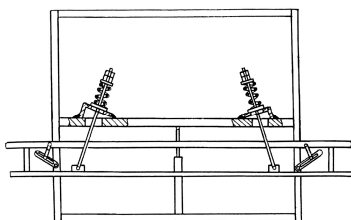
Схема пружинной А-образной маятниковой навески штангового опрыскивателя [38, 77]
